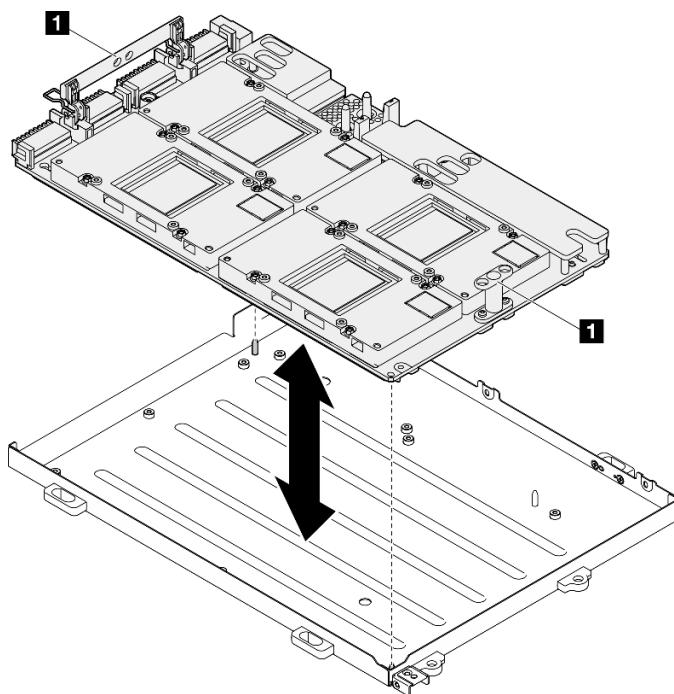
Extracción del Conjunto de placa de GPU SXM5
